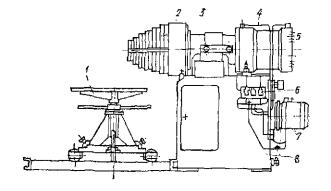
Установка для калибровки труб и деталей трубопроводов:
